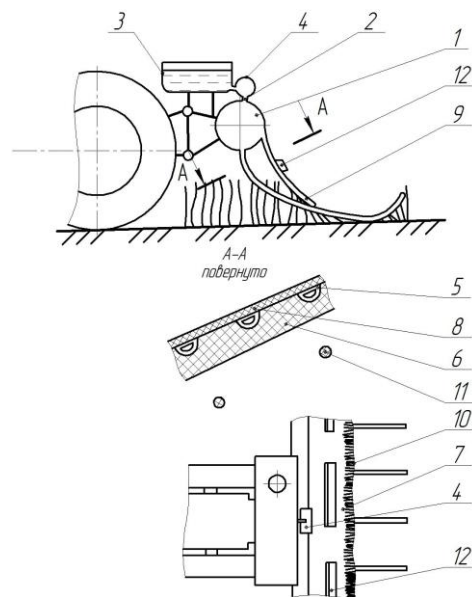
Пристрій для нанесення отрутохімікатів на рослини: 1 - штанга; 2 - шланги; 3 - бак; 4 - вентиль; 5 - периферійна трубка; 6 - пористий шар ґноту; 7 - ґніт; 8 - еластичний шар; 9 - робочий кінець ґноту; 10 - бахрома; 11 - пружні елементи; 12 - вантажі
